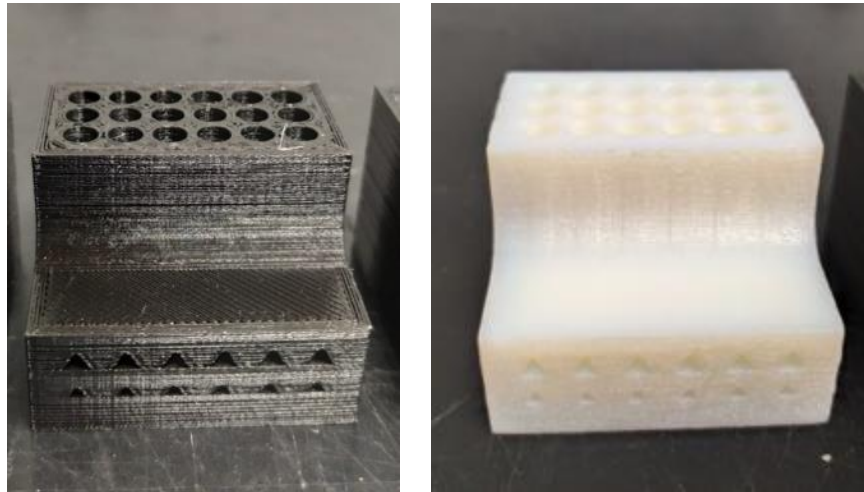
Pieza fabricada mediante FDM (izquierda) y polyjet (derecha)
